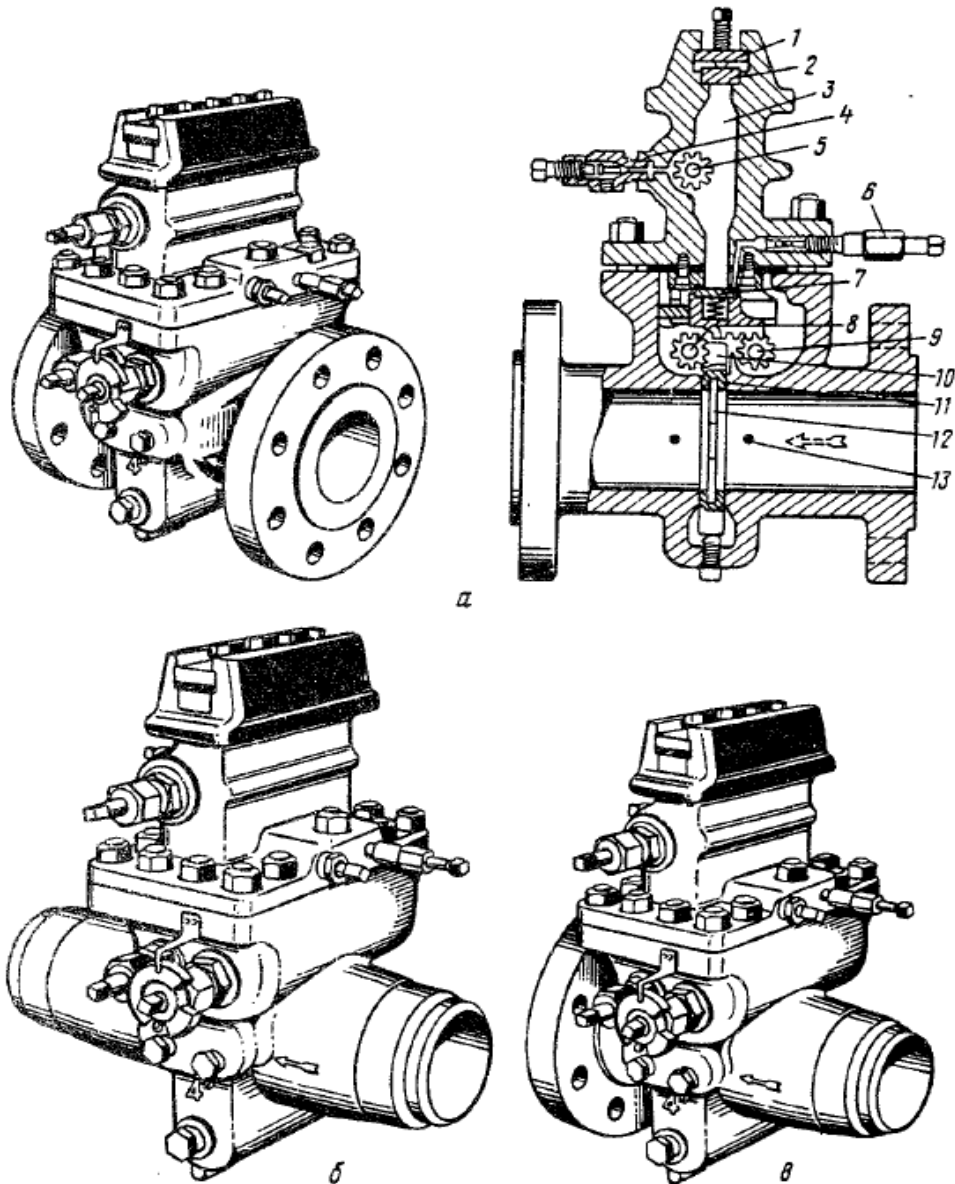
Двухкамерные диафрагменные фитинги с фланцевым (а), сварным (б) и смешанным (фланцево-сварным) соединениями с трубопроводом:
